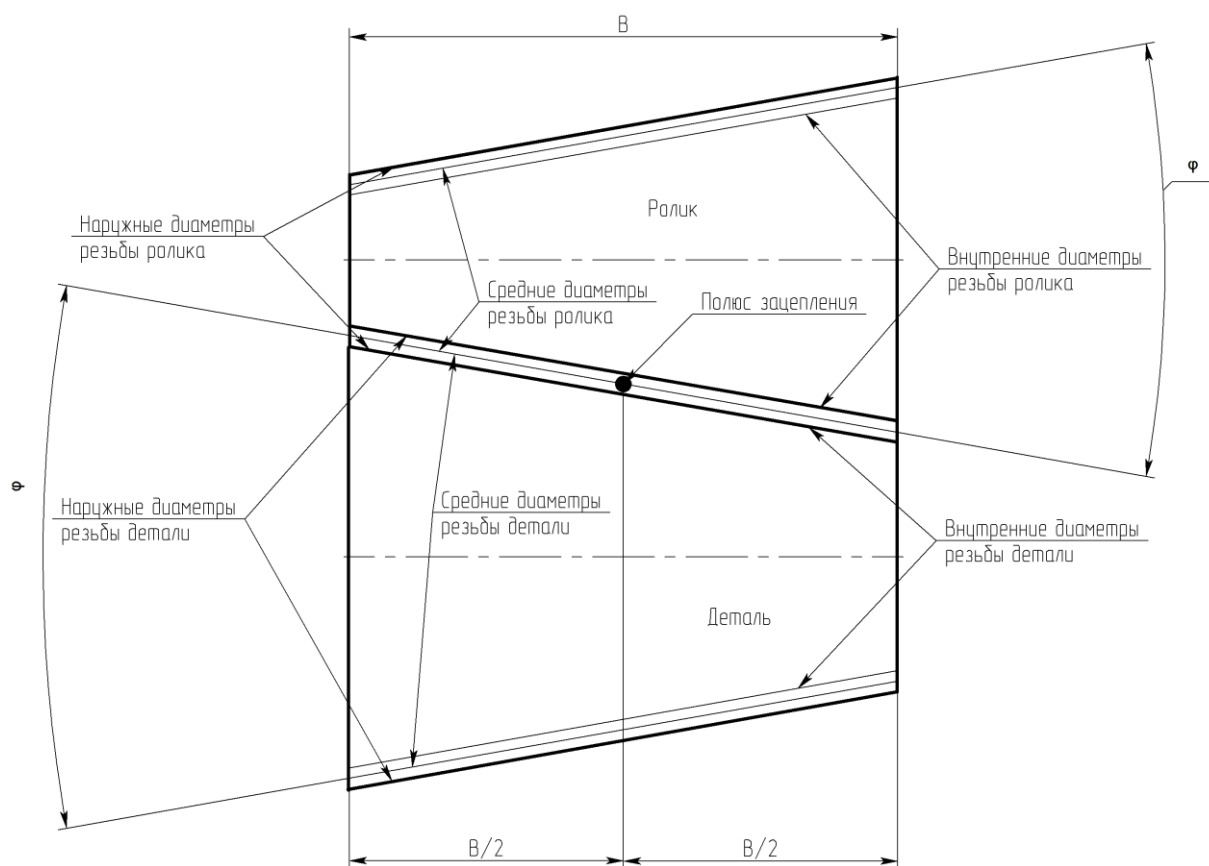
Схема накатывания конической резьбы коническими роликами с параллельными осями инструмента и заготовки
